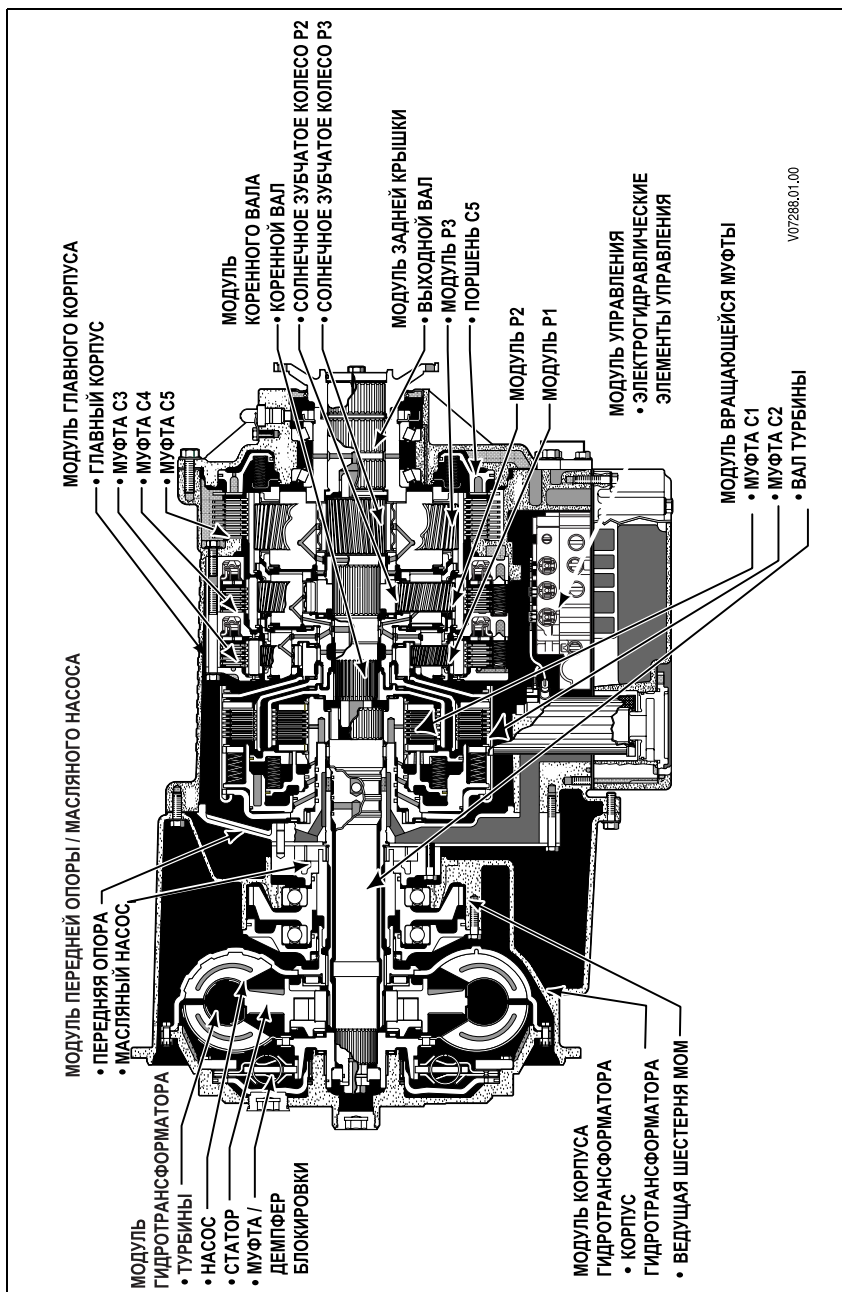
Коробки передач серии 4000 — поперечный разрез
